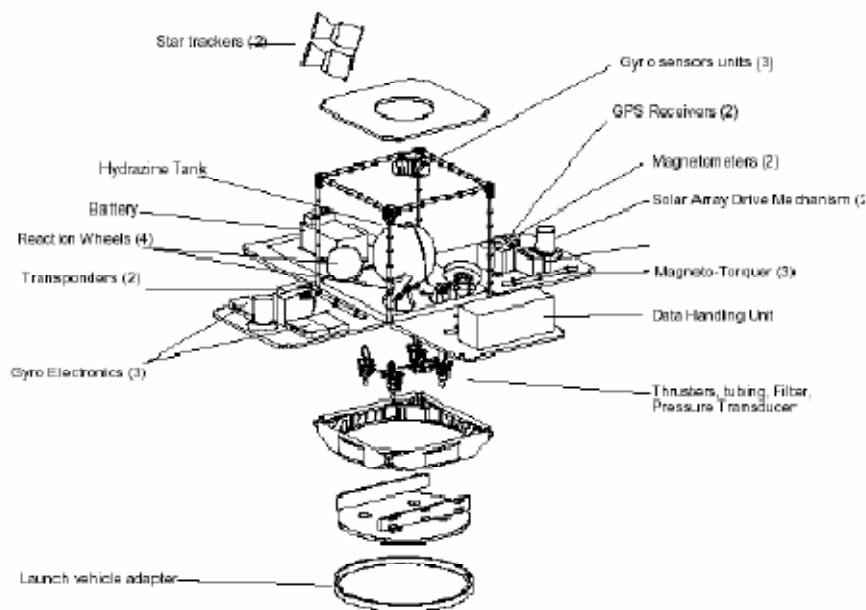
Vue éclatée de la plate-forme PROTEUS
